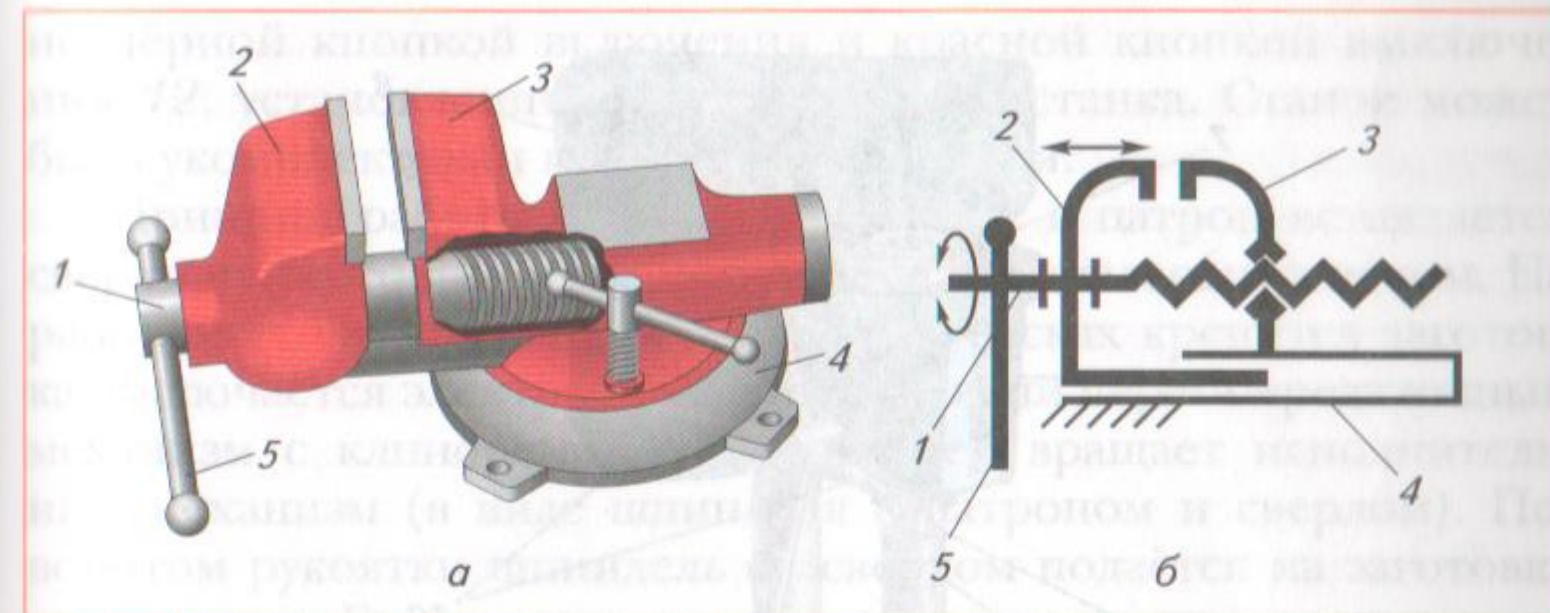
Тиски: а — устройство тисков; б — кинематическая схема тисков; 1 — винт; 2 — подвижная губка; 3 — неподвижная губка; 4 — опорная плита; 5 — рукоятка
